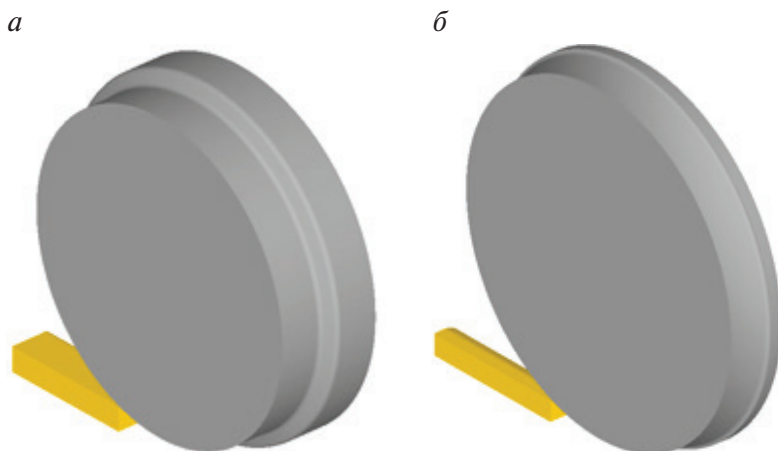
Вид созданных и ориентированных моделей заготовки и вала:
